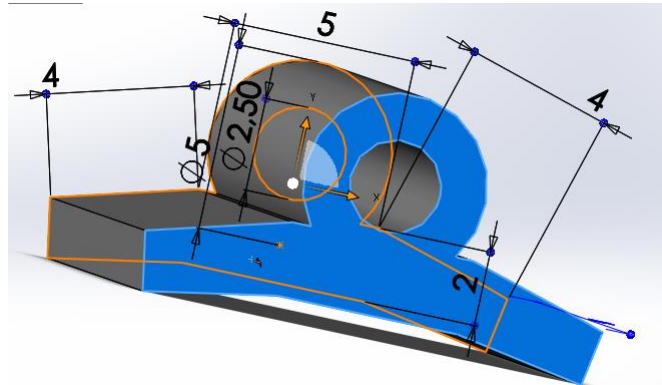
Diseño y dimensiones del guarda cables realizado en SolidWorks
